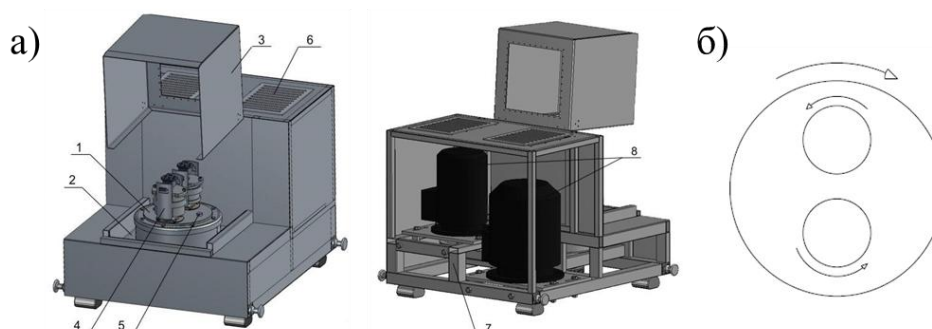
Установка планетарной мельницы «Активатор 2S» (а) и направление вращения корпуса и барабанов (б)
